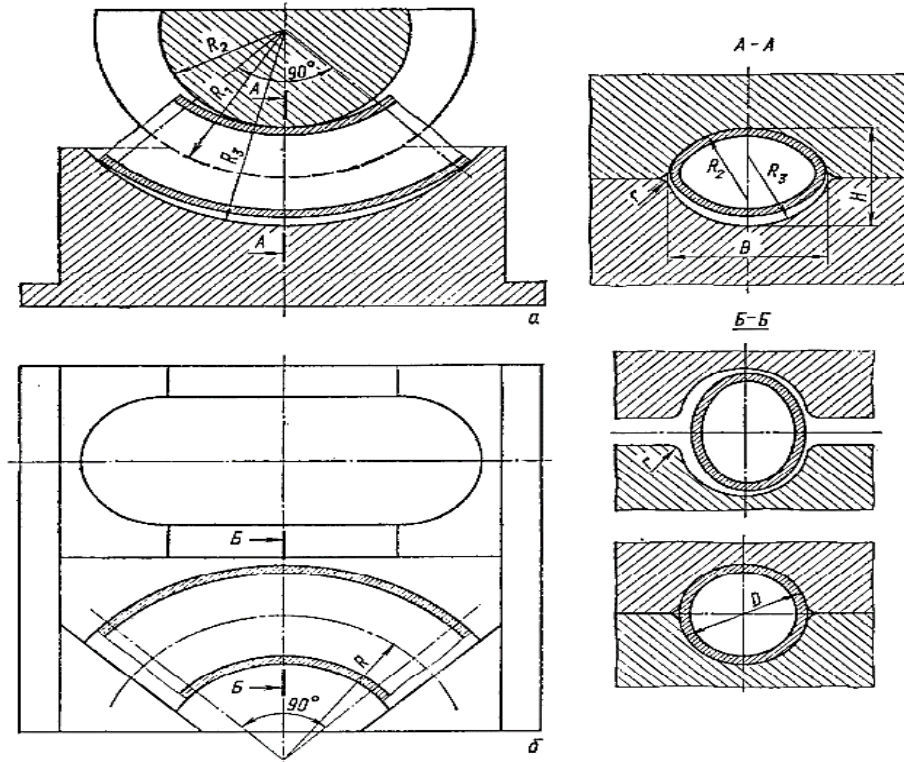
Спосiб деформування труби при штампуванні
